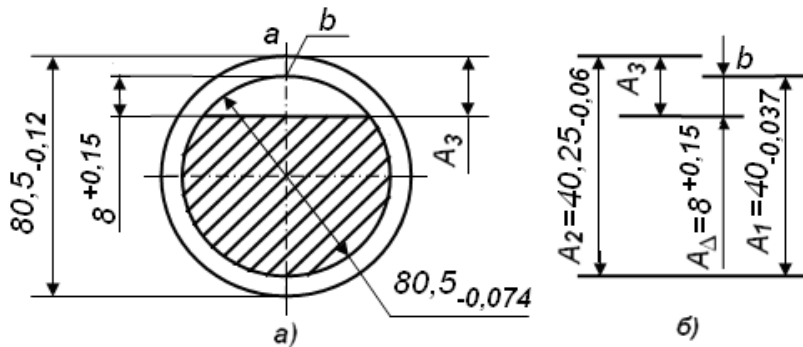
Ескіз вала (а) і розмірний ланцюг (б)
